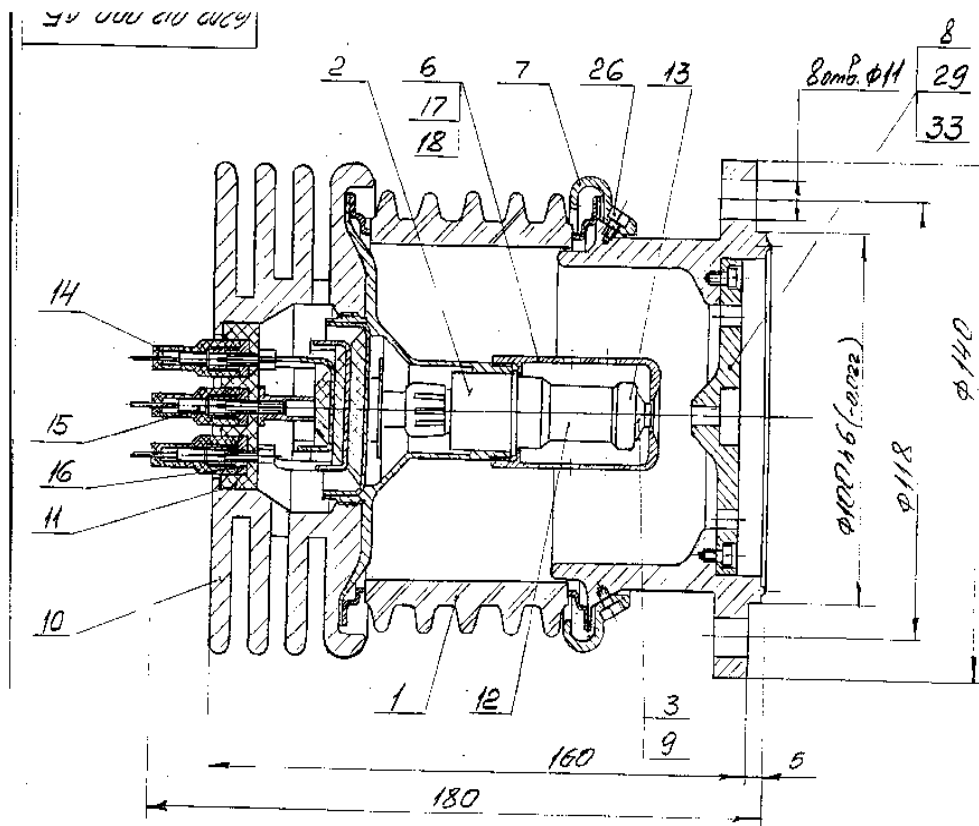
Сборочный чертеж источника электронов линейного ускорителя.
